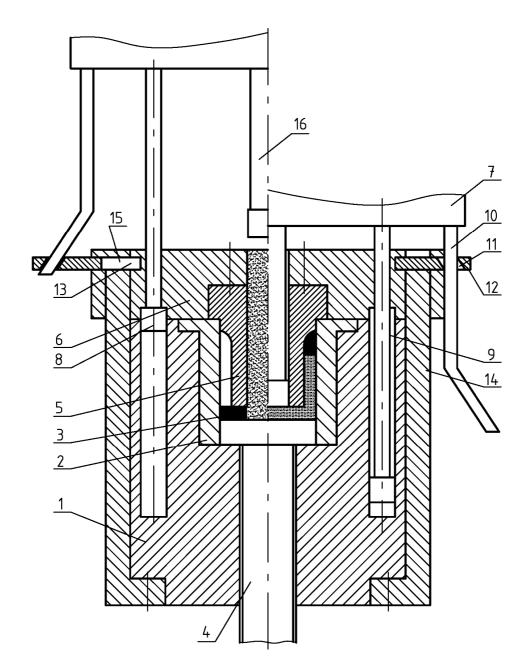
Пресс-форма для выдавливания полых изделий из гранул алюминиевых сплавов 1 — нижняя плита; 2 — основная матрица; 3 — сменное кольцо; 4 — нижний пуансон; 5 — дополнительная матрица; 6 — верхняя плита; 7 — траверса; 8 — тяги верхней плиты; 9 — направляющие; 10 — клин-пальцы; 11 — наклонные отверстия; 12 — ползуны; 13 — горизонтальные пазы; 14 — тяги нижней плиты; 15 — горизонтальные отверстия; 16 — верхний пуансон
